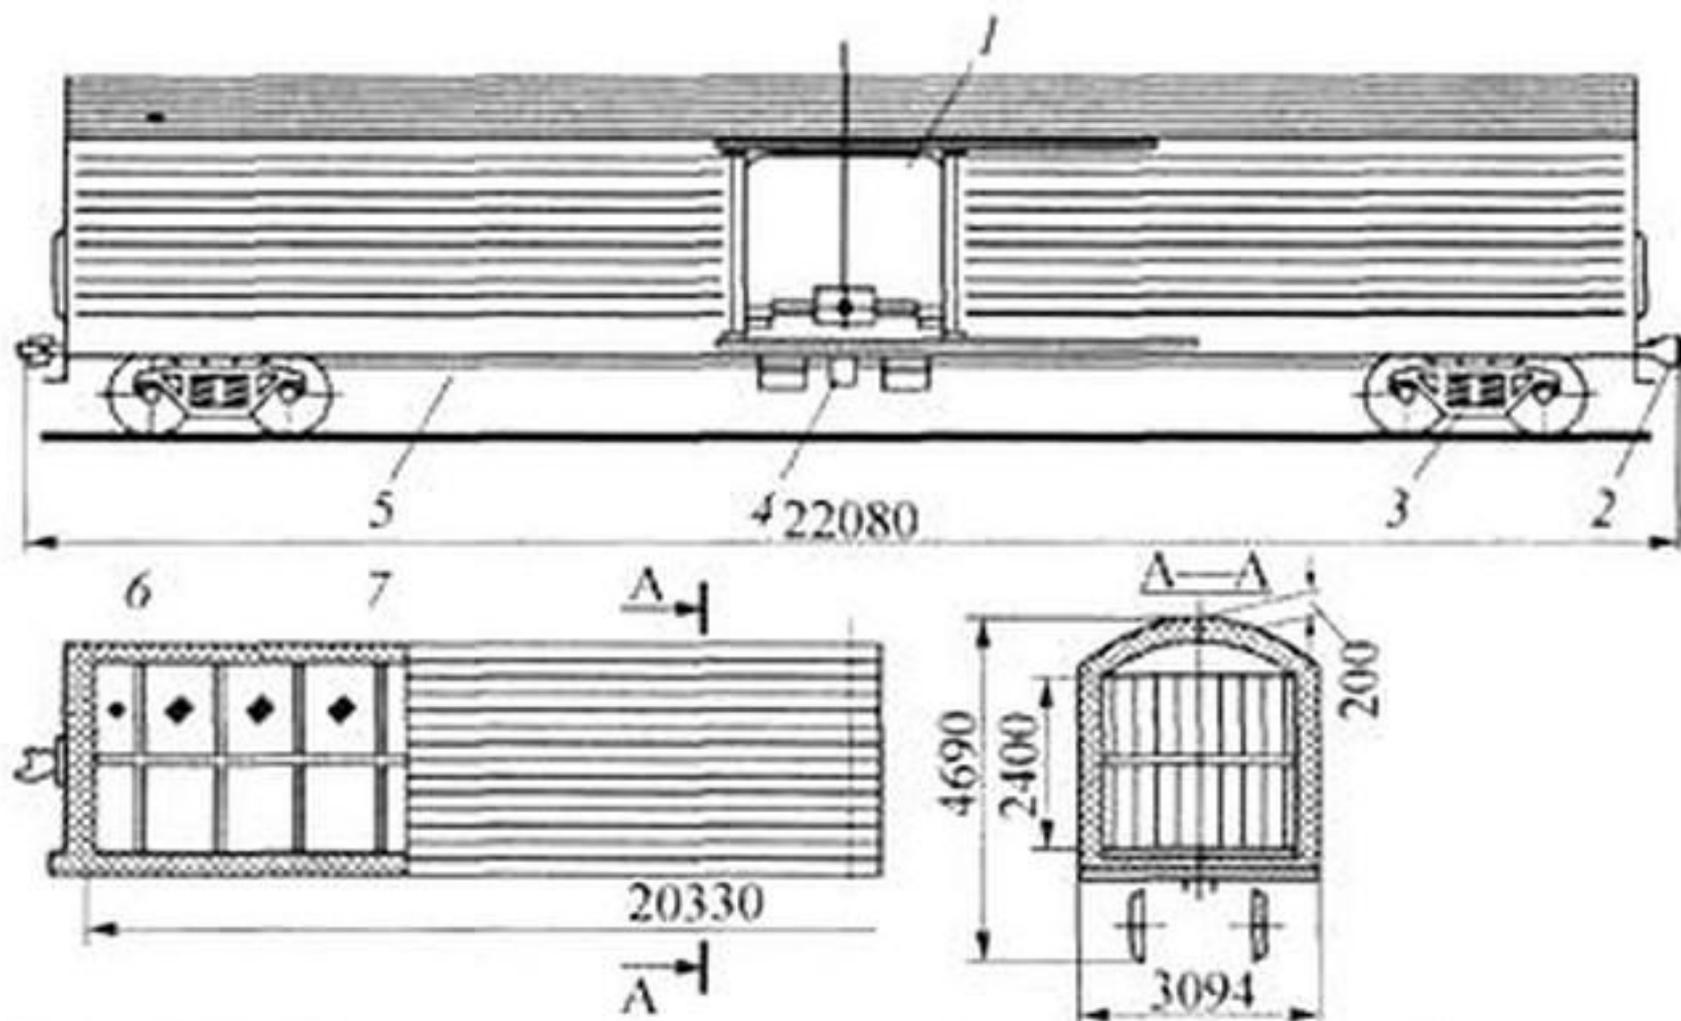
Вагон-термос: 1 — дверь; 2 — автосцепка; 3 — тележка; 4 — пневматический тормоз; 5 — стояночный тормоз; 6 — защитная стенка; 7 — напольные решетки
